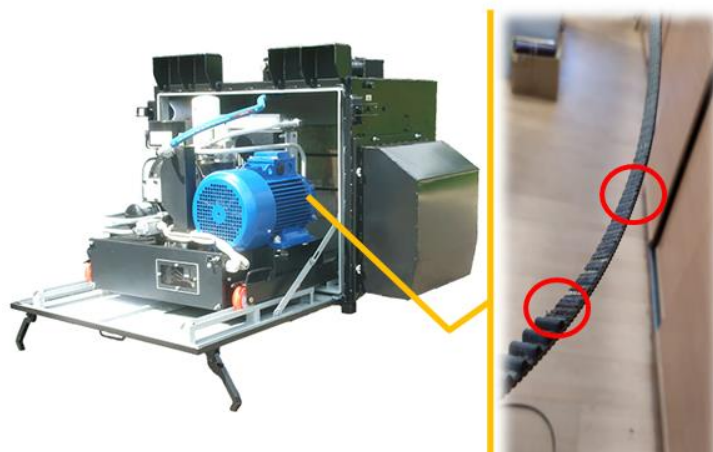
Внешний вид компрессора ВКУ-0,6-ЭП-0,1 и характерные повреждения приводного ремня
